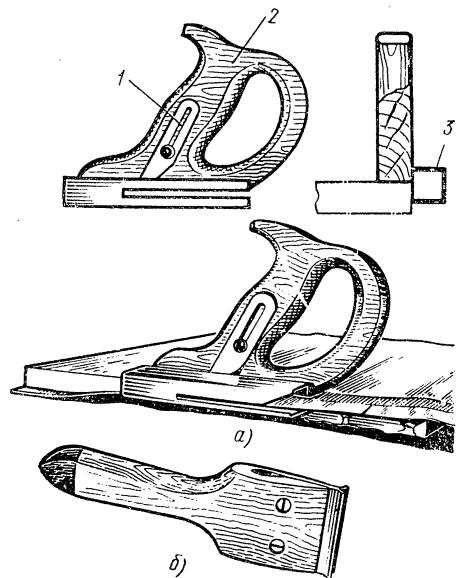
Приспособления для снятия свесов шпона (а) и kleевой ленты (б) в заготовках после их облицовывания:
